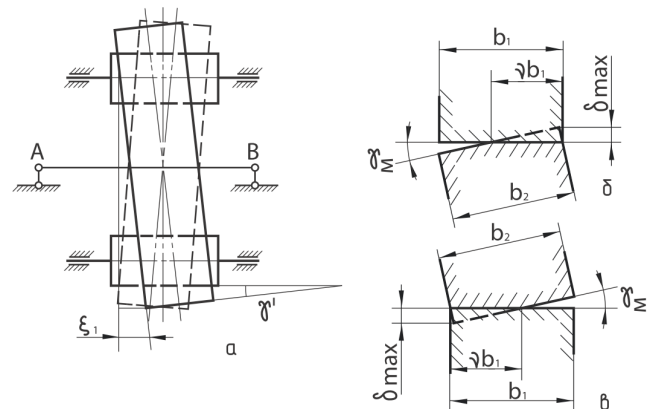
Характерні випадки взаємного розташування елементів вінцевої зубчастої пари у випадку прямолинійної осі обертання корпусу обертового агрегату:
